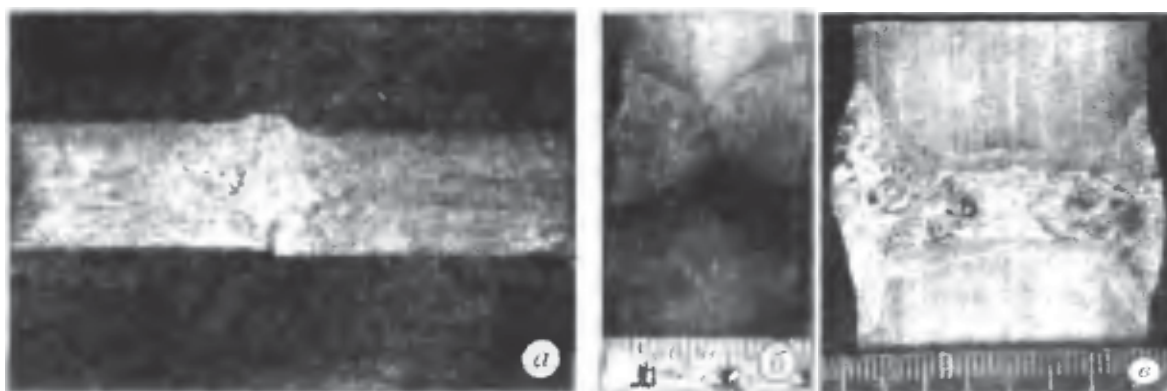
Сварные швы с непроварами (сталь, макроструктуры):
